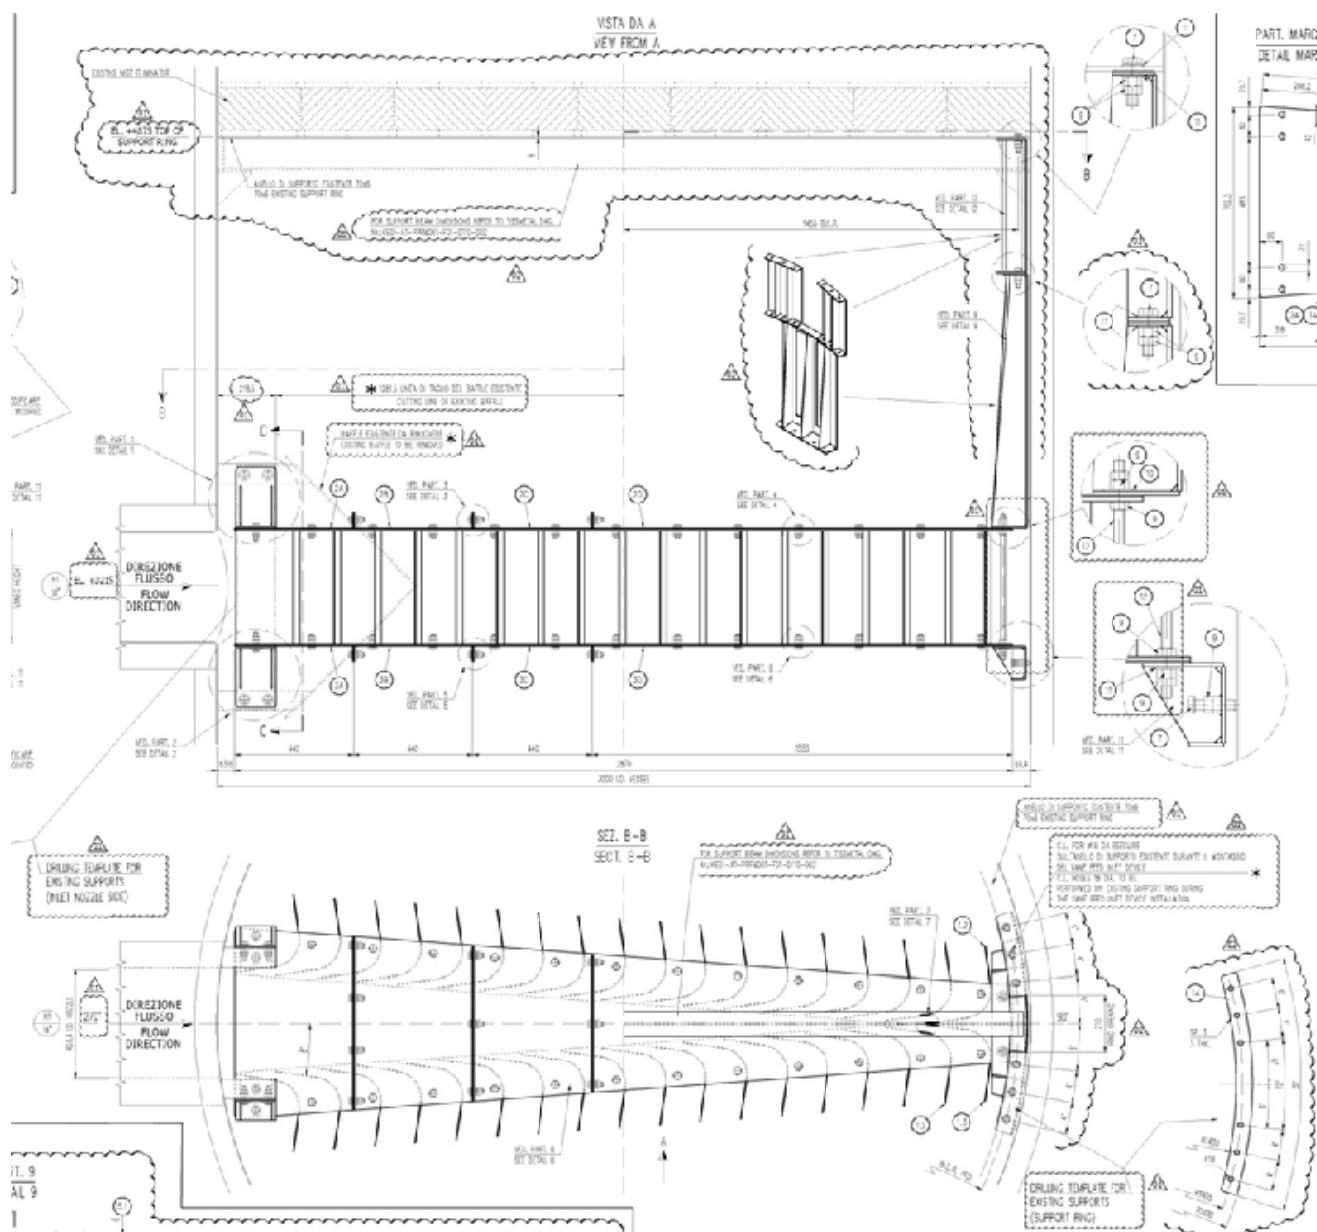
8. Питающее устройство лопастного типа. Фрагмент чертежа KE01-A1-P3JM01A-F01-0001-000-PR18042.
